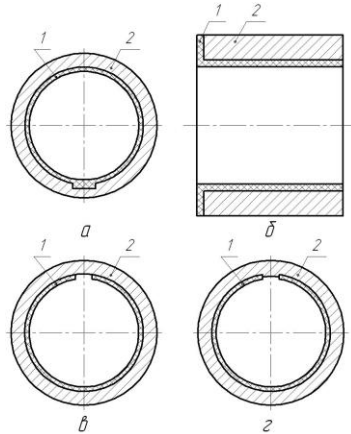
Схеми кріплення в корпусі підшипника втулок з термопластичних пластмас: 1 – втулка; 2 – корпус
